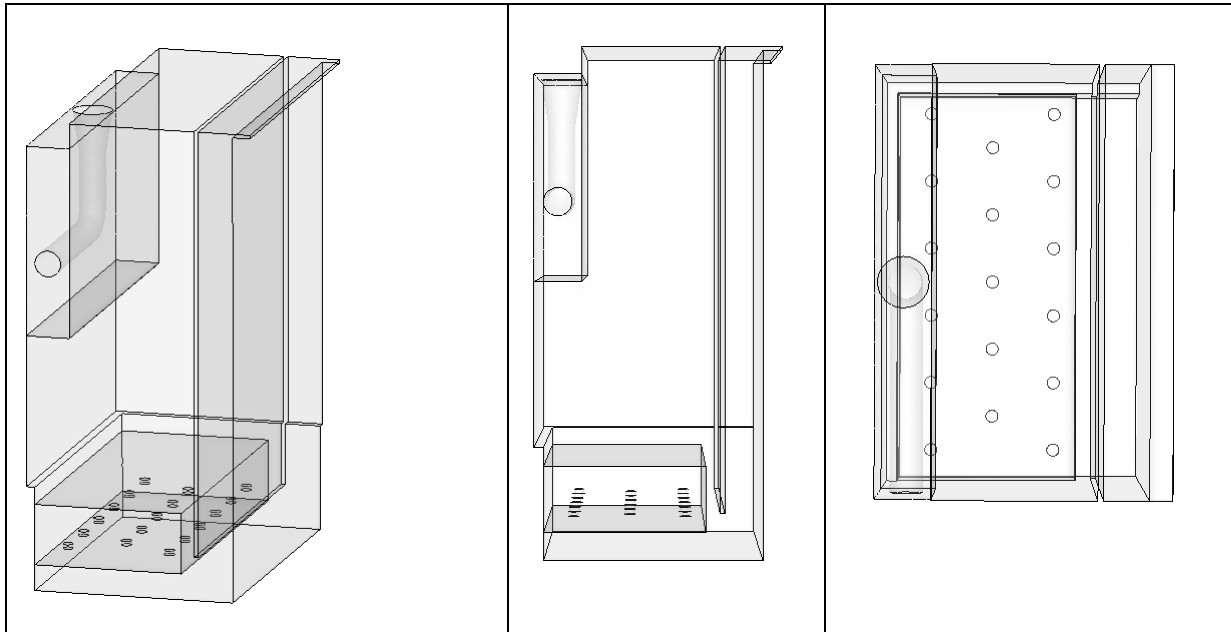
Geometrie Grundvariante GV2. Links: 3D-Ansicht. Mitte: Seitenansicht. Rechts: Draufsicht.
